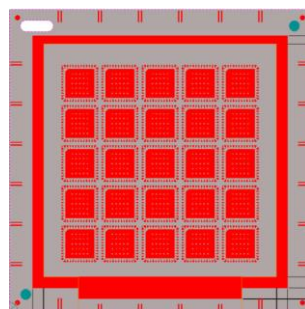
Design der Top-Lage eines QFN-FlexPac-LN mit einem Metallrahmen, auf dem im FAM-Prozess die Dichtflächen des Werkzeugeinsatzes aufliegen.
